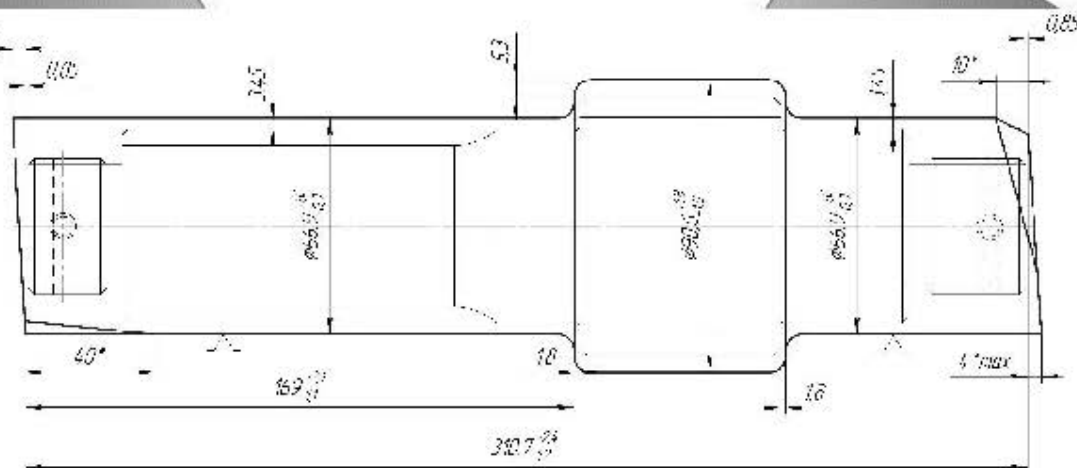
Заготівка – штамповка на ГКМ
